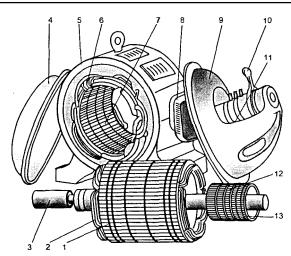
Асинхронный электродвигатель с фазным ротором: 1 — сердечник ротора; 2 — обмотка ротора; 3 — вал; 4 — подшипниковый щит со стороны привода; 5 — корпус статора; 6 — обмотка статора; 7 — сердечник статора; 8 — коробка выводов; 9 — подшипниковый щит со стороны контактных колец; 10 — рычаг короткозамыкающего приспособления; 11 — щеткодержатели внутри щита 9; 12 — контактные кольца; 13 — смещающееся вдоль вала кольцо короткозамыкающего приспособления
